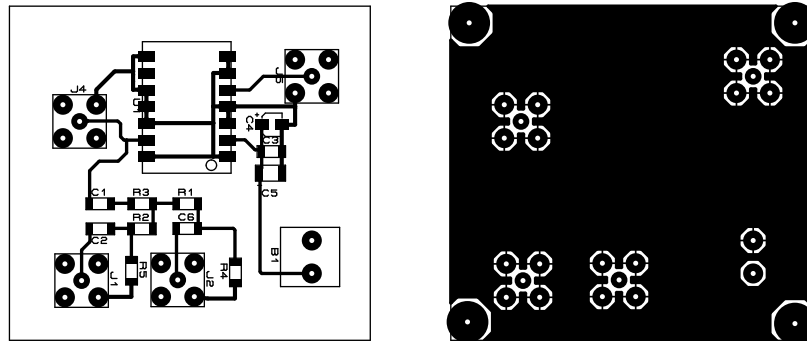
Layout vue de dessus et de dessous de la partie VCO
